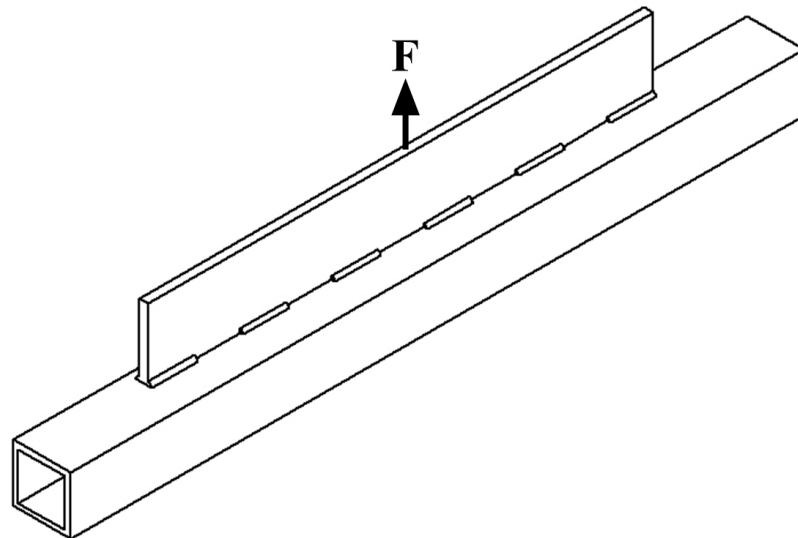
Desenho esquemático da chapa soldada no tubo quadrado.
